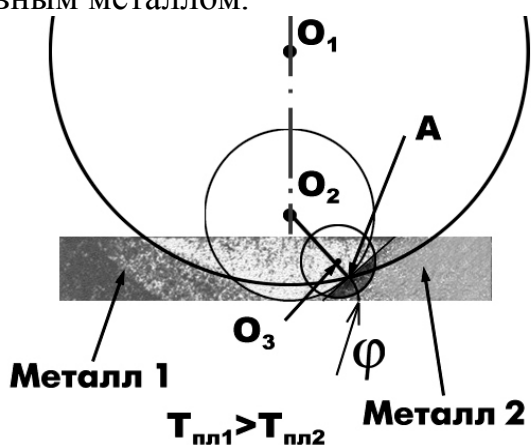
Модель схемы сварки разнородных металлов
